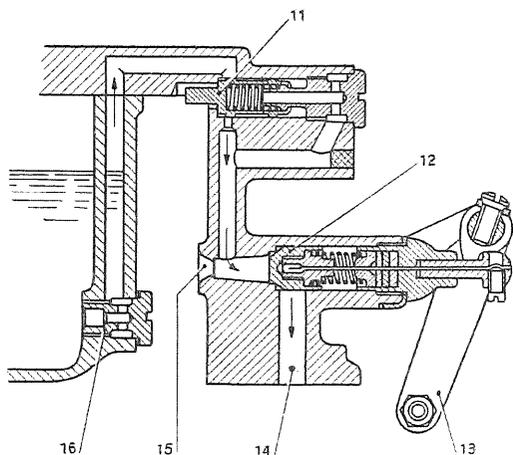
Sezione del dispositivo d'avviamento del carburatore Zénith 26 VF.
